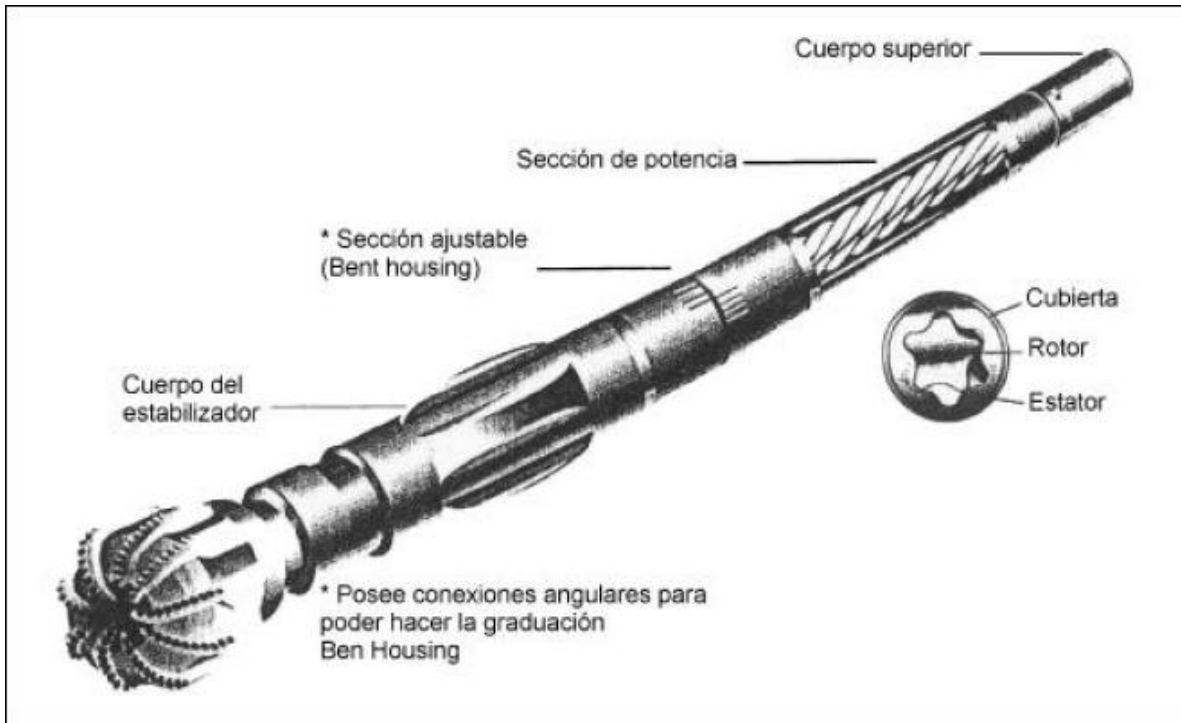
Ensamblaje típico de BHA con Motor de Fondo
